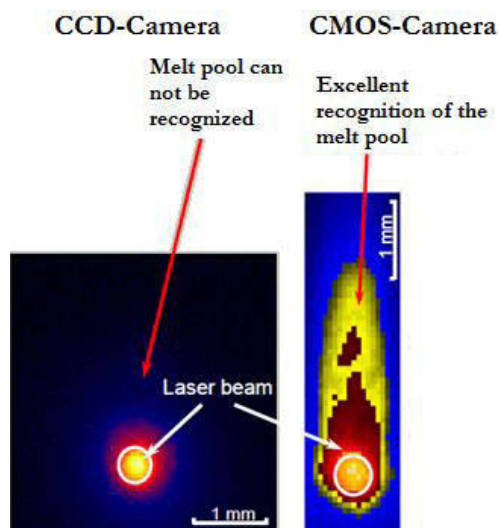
Comparatif entre caméra CCD et CMOS appliqué dans le contrôle en ligne de la soudure laser [60]
